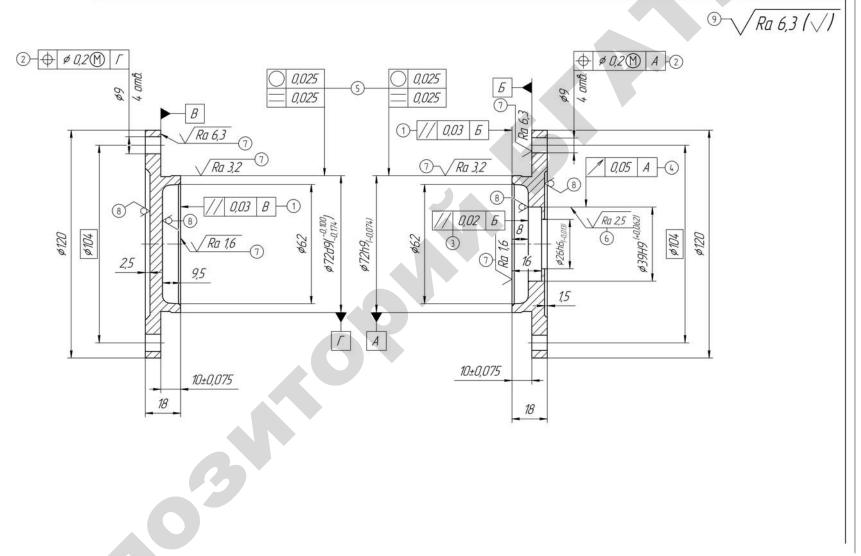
Схема простановки размеров и показателей точности для крышек подшипников
